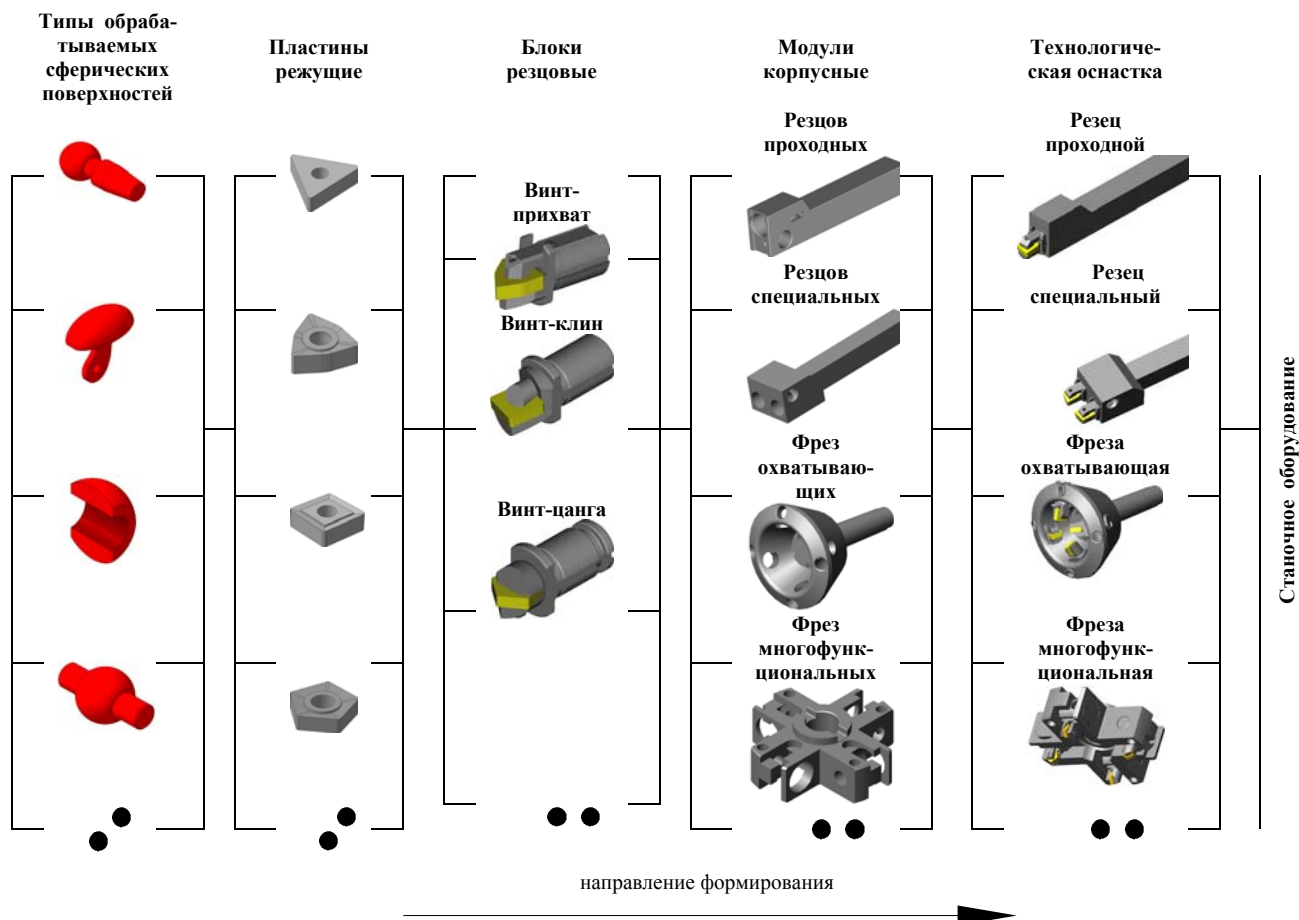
Схема формирования блочно-модульного режущего инструмента
